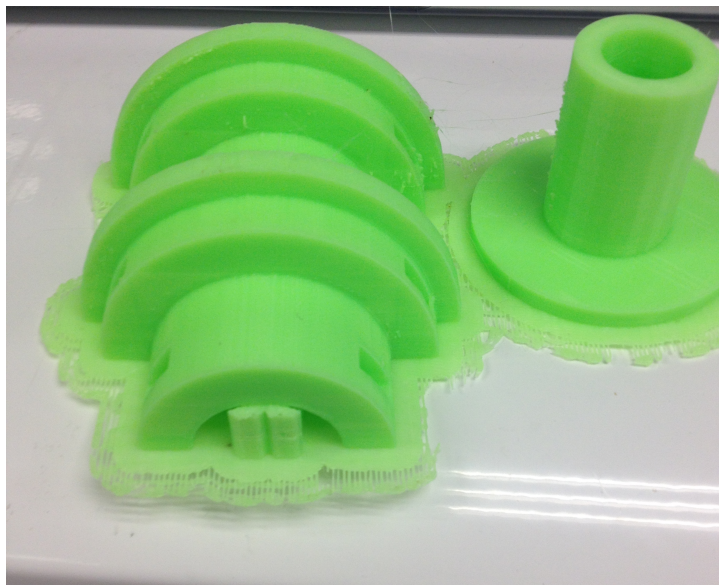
Fabricación del Molde. Vista isométrica del molde acabado. (Fuente: Propia)
